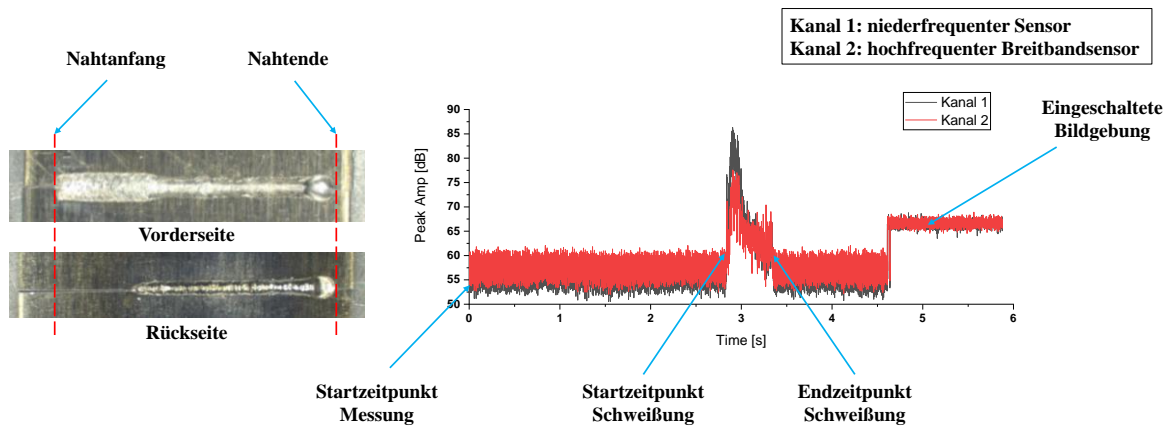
Schweißnahtober- und Schweißnahtunterraupe einer teilweise unvollständigen Durchschweißung (links) und Übersicht über die zeitlichen Messdaten (rechts)
